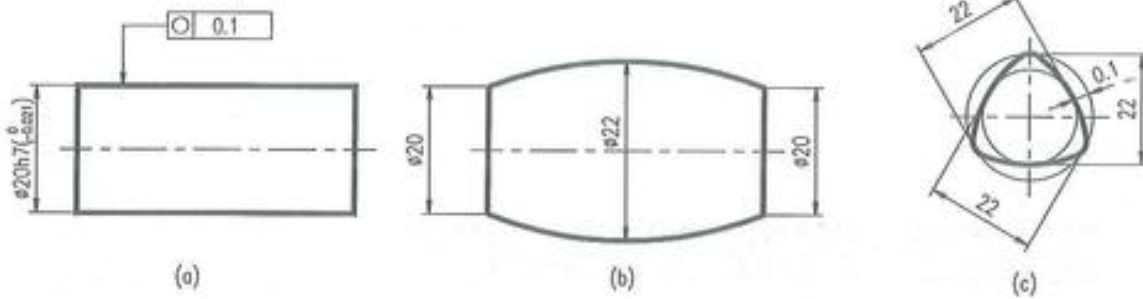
(a) Especificación de tolerancias geométricas en un cilindro. (b y c) Piezas que cumplen la tolerancia de redondez y no tolerancia dimensional.
